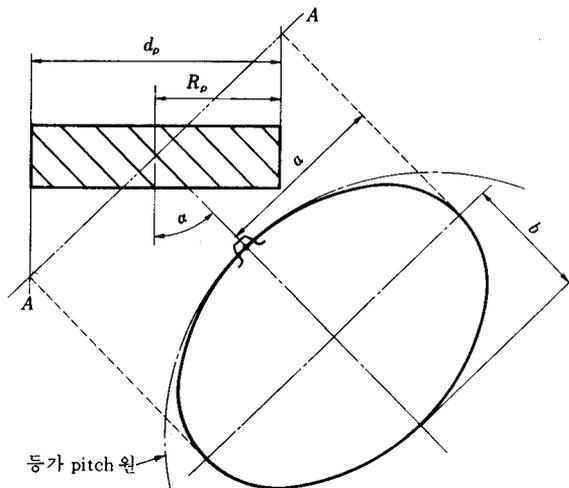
helical gear의 齒線 방향에 직각인 단면
